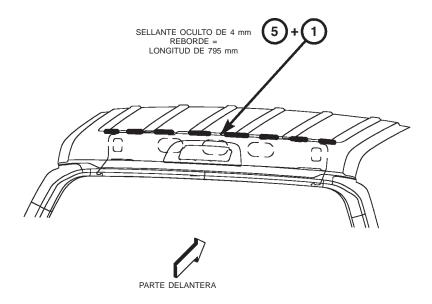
PLANCHA SUPERIOR DEL TECHO TRASERA Y PLANCHA DE TECHO
